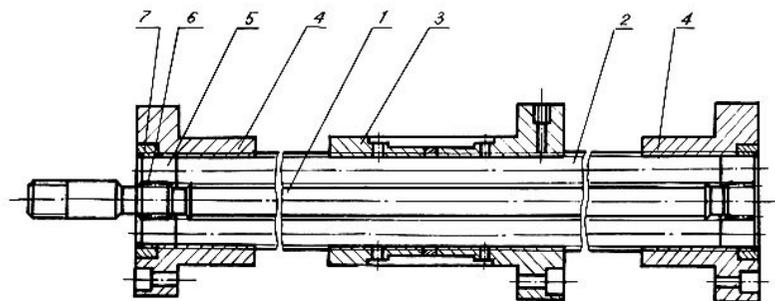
Планетарная передача с длинными резьбовыми роликами
